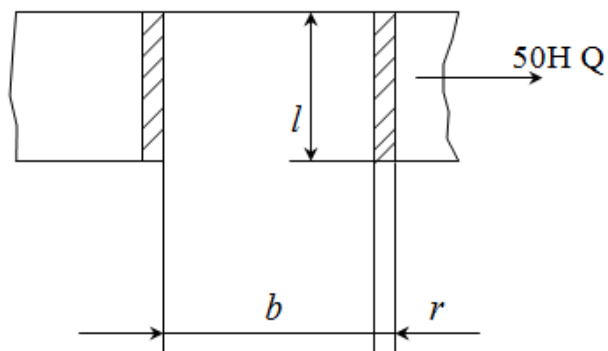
Схема для розрахунку зварного з'єднання
